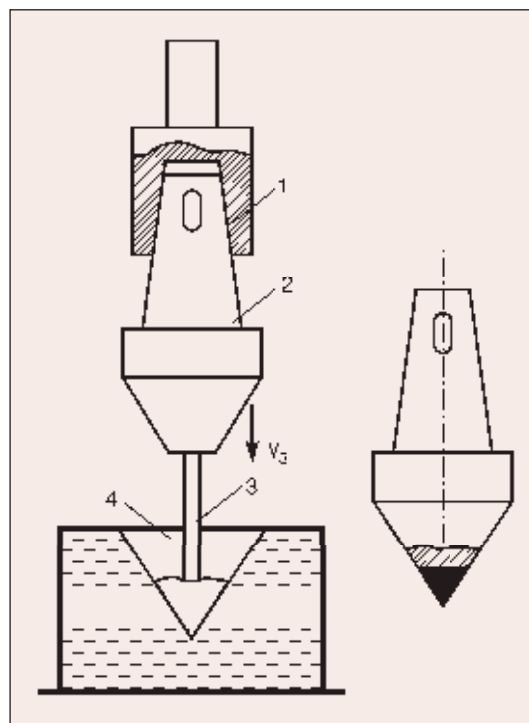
Схема стыкошлаковой наплавки: 1 — плавящийся электрод; 2 — патрон для закрепления детали; 3 — наплавляемый керн; 4 — кристаллизатор
